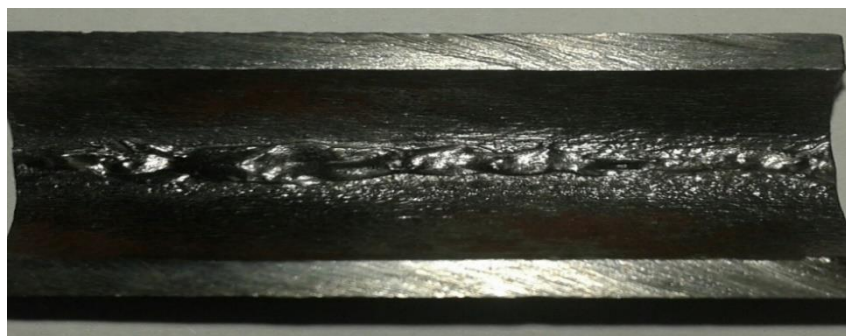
разрез трубы диаметром 21,3мм, вид внутреннего шва сверху
